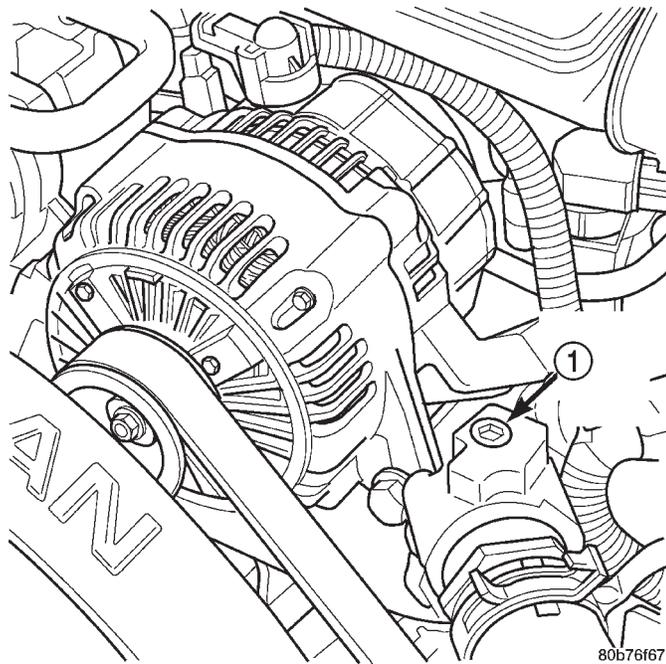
Kühlsystem-Entlüftungsschraube—4.7L
